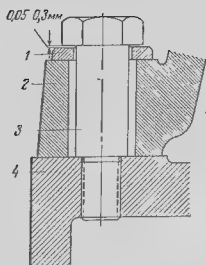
Крепление скользящей лапы к фундаментной плите.
